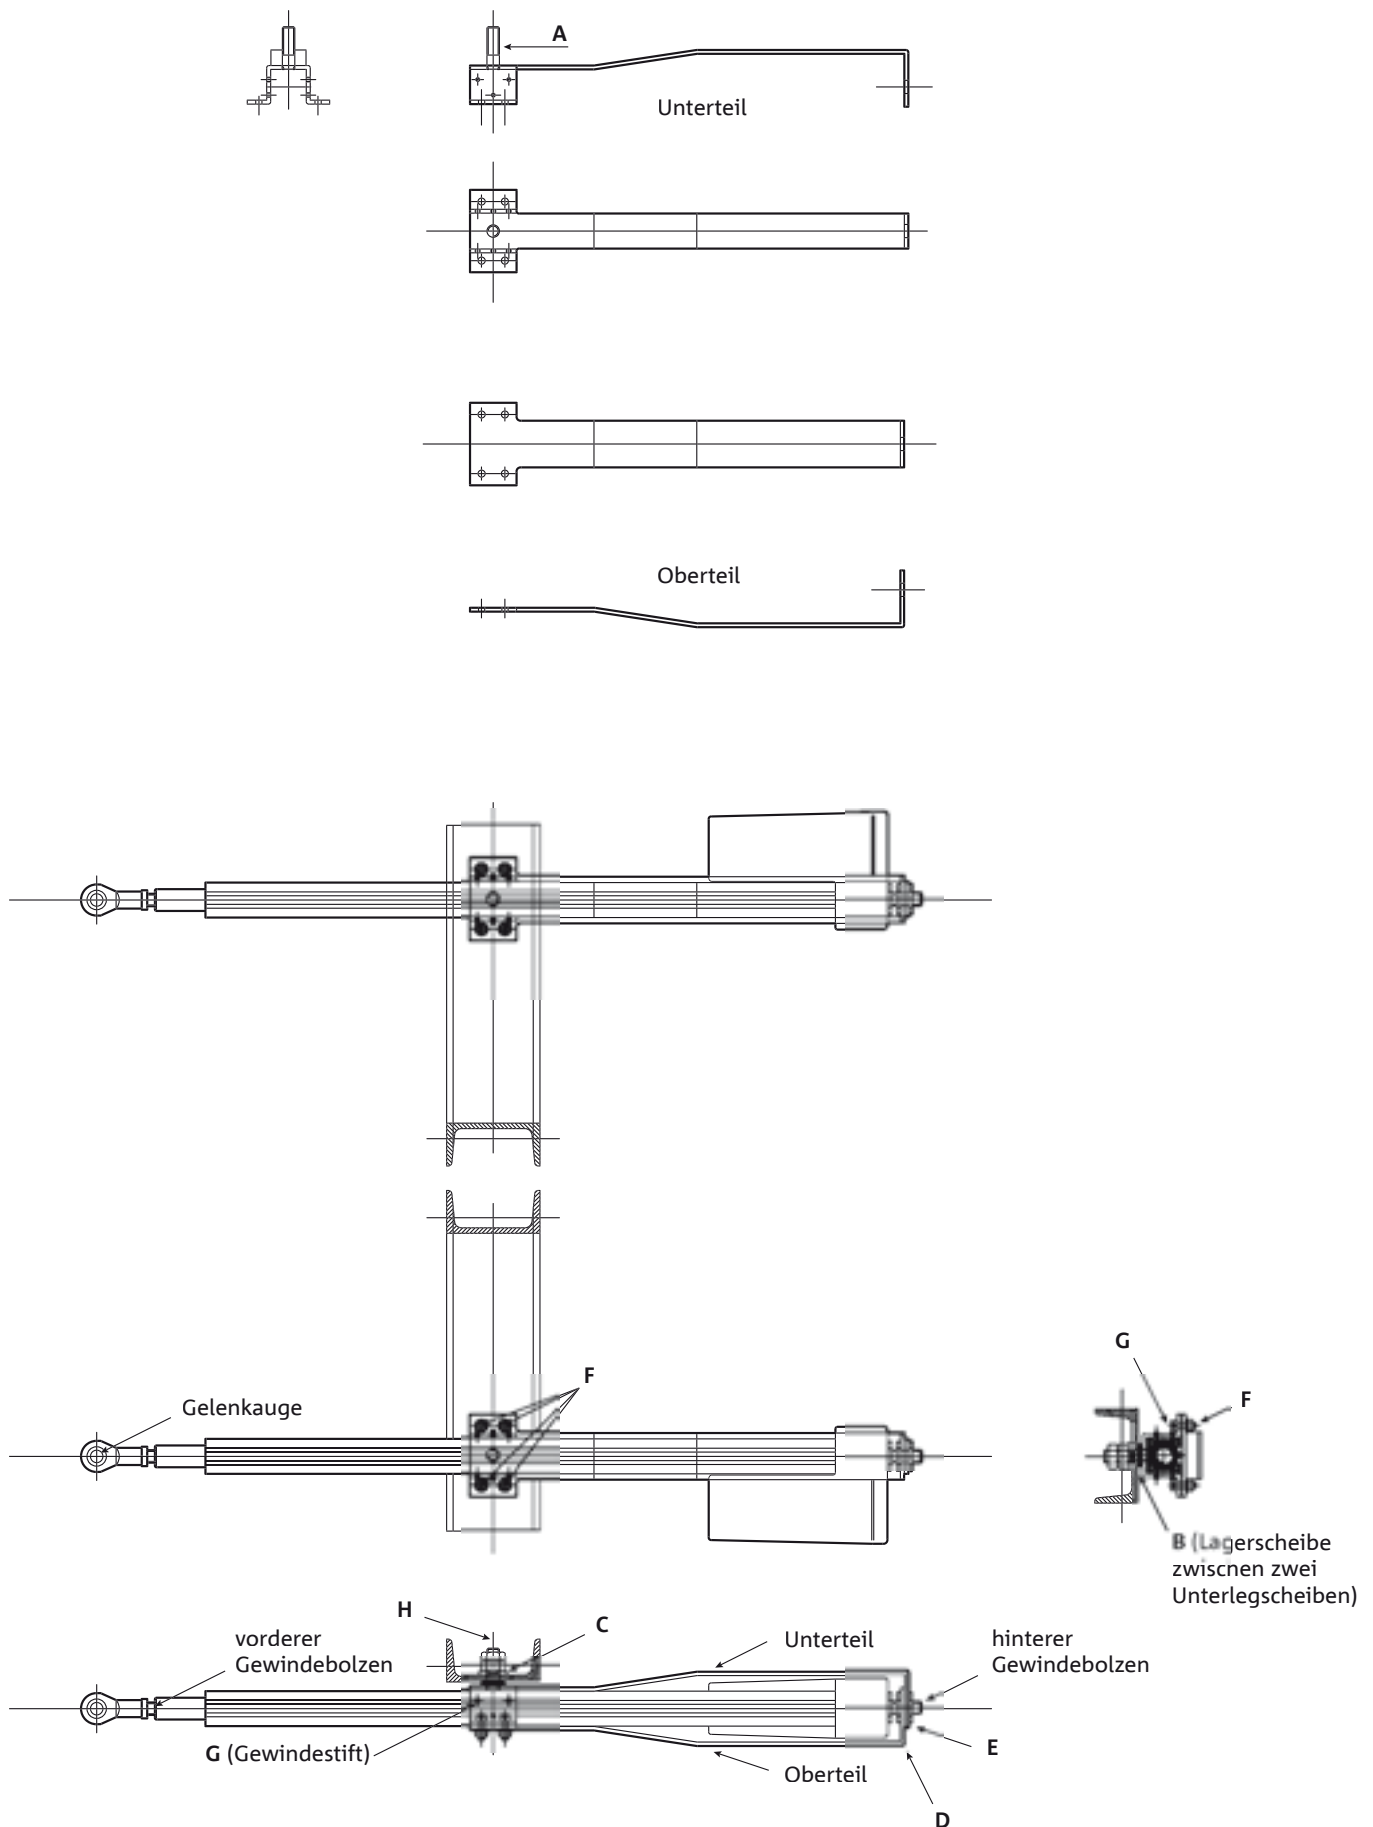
Motorhalterung und deren Befestigung am Motorträger
